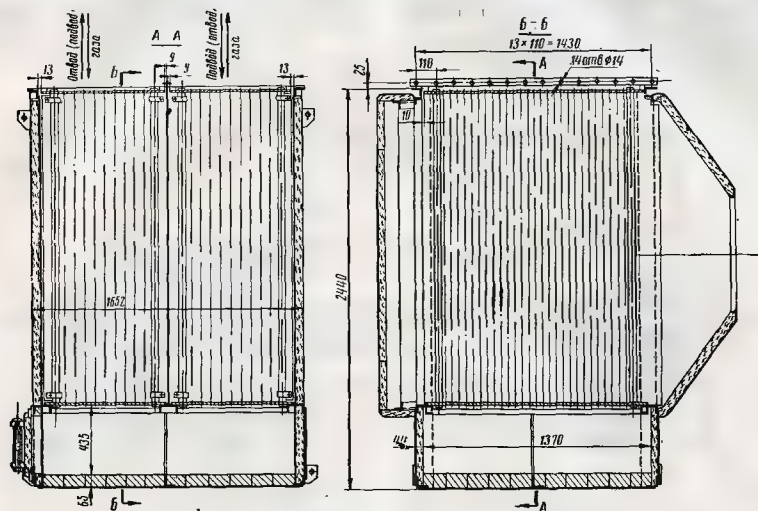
Воздухонагреватель трубчатый двухходовой с поверхностью нагрева 140 м<sup>2</sup>
